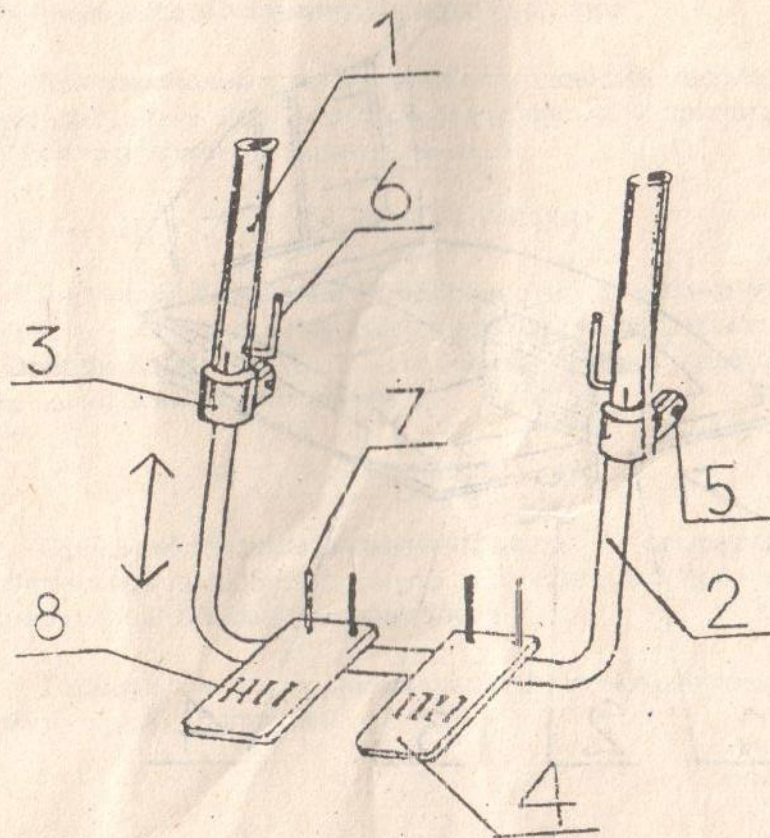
Подножка: 1 - корпус; 2 - подножка; 3 - хомут; 4 - опора для стопы; 5 - болт; 6 - крючок; 7 - стойка; 8 - щелевидные отверстия.
